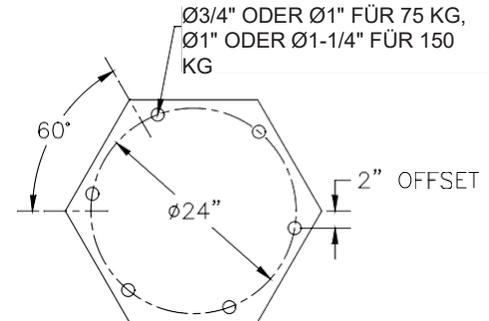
C. Sockelbolzenmuster mit 6 Bolzen.
